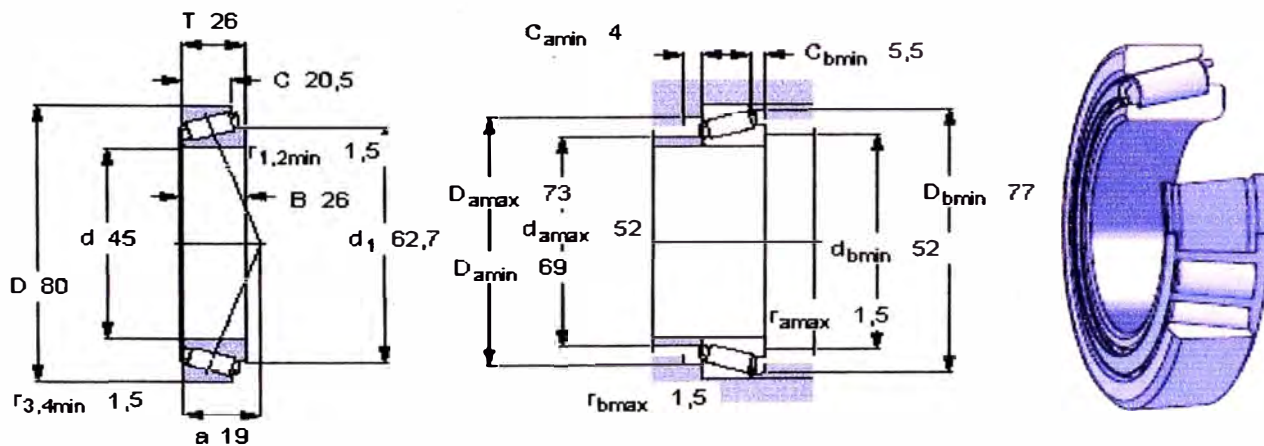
Dibujo y dimensiones del rodamiento de bolas.
